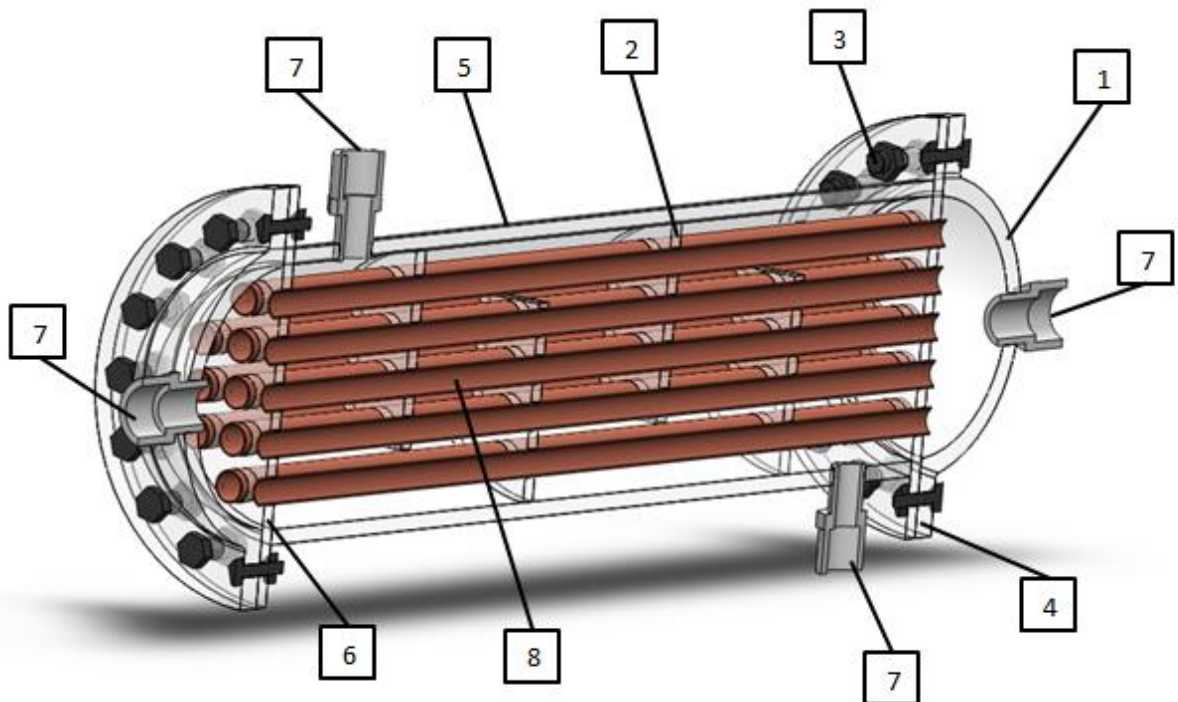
Componentes mecánicos del intercambiador de calor de tubos y coraza, Fuente Solidworks 2014
